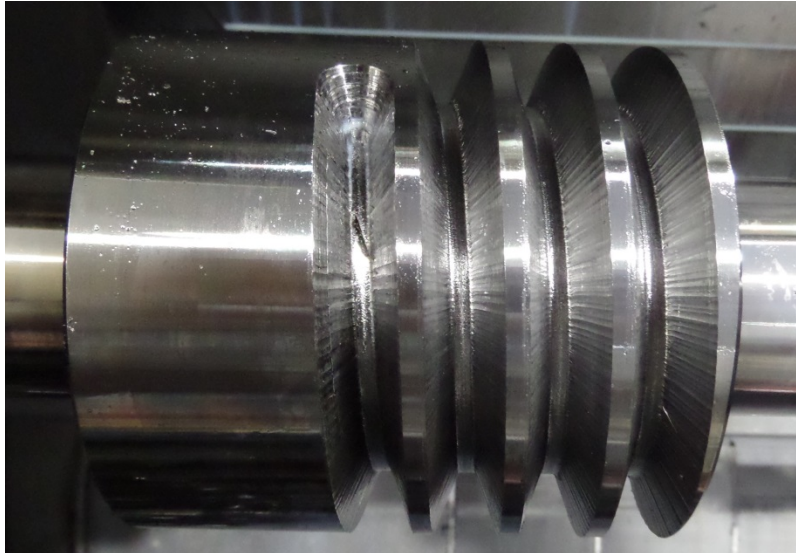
Odvalovací fréza po obrobení dle druhého způsobu
